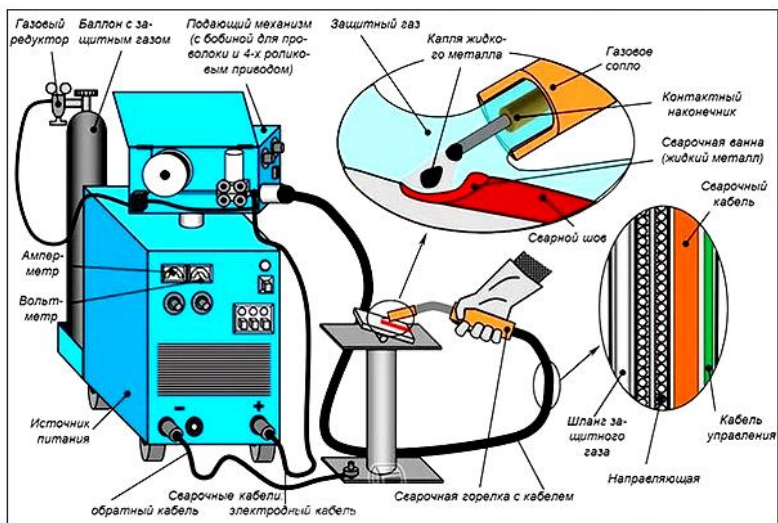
Схема полуавтоматической сварки в среде углекислого газа CO_2 [2]
